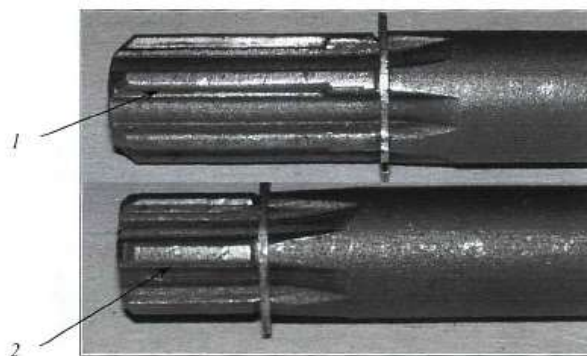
Изношенные поверхности шлицев валика 700А.17.00.038-3 (1 – шлицевая часть вала, соединяемая с шестерней конического редуктора; 2 – шлицевая часть вала, соединяемая с втулкой привода насоса)
